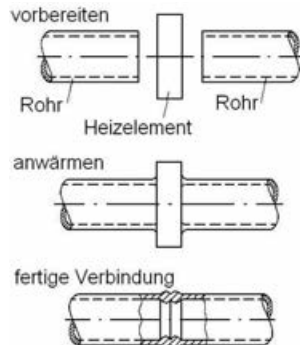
Prinzip des Heizelementstumpfschweißens am Beispiel Rohr.
